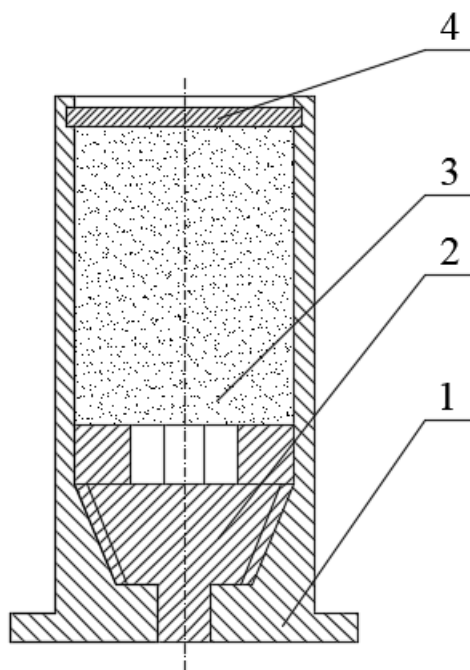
Піропатрон удосконалений: 1 – корпус; 2 – електрозапалювач; 3 – порохова суміш; 4 – заглушка
